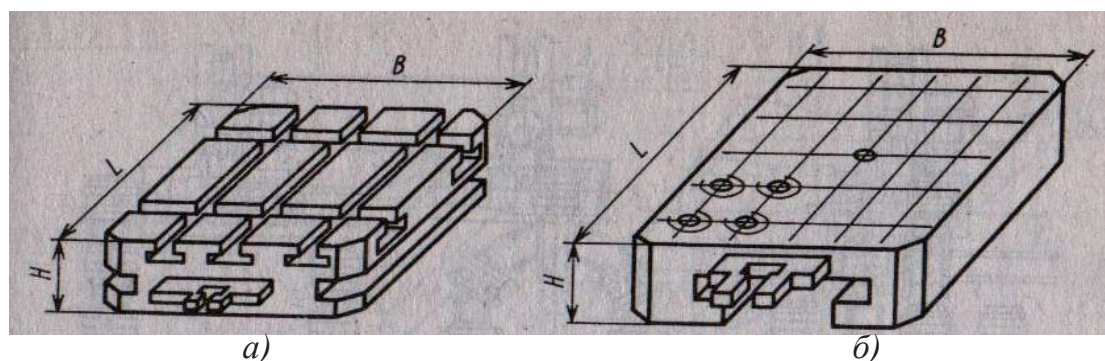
Конструктивное исполнение рабочей поверхности спутников: *а* – с системой т-образных пазов; *б* – с сеткой резьбовых отверстий
